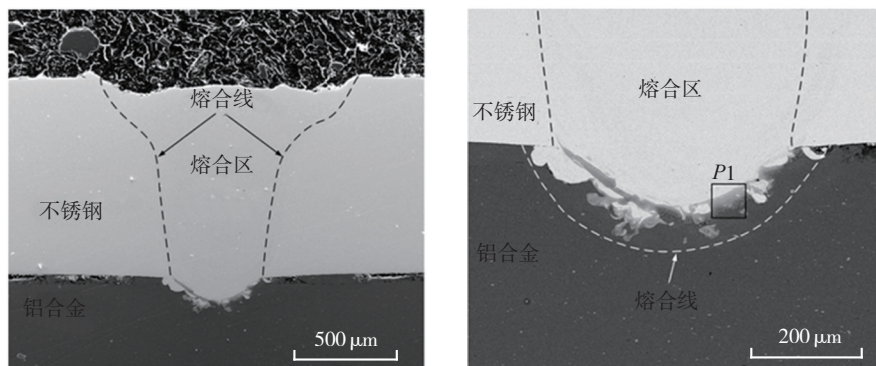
激光深熔焊接钢/铝异种接头横截面形貌
